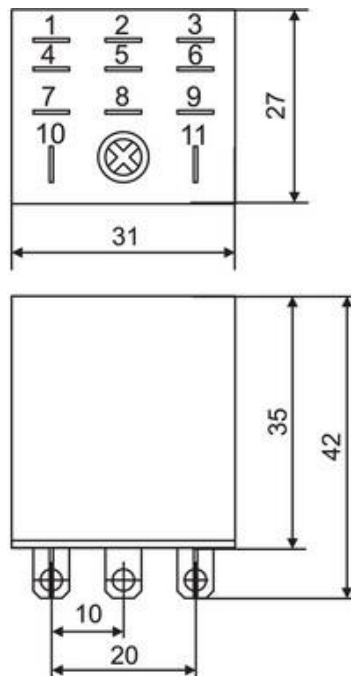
Габаритные размеры реле РЭК77/3
